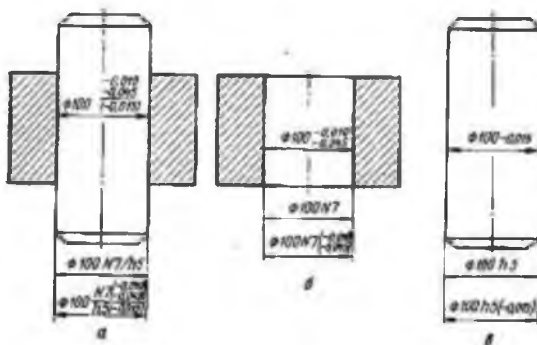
Примеры обозначений полей допусков и посадок на чертежах:
